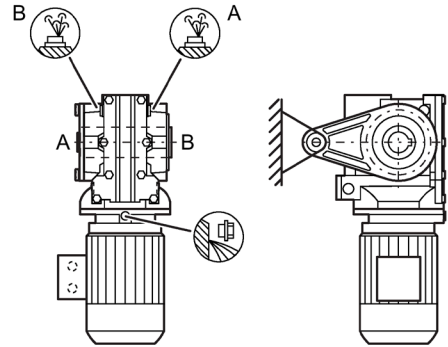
Einbautagen für Kegelradgetriebe KAD Aufsteckausführung Baugrößen 39 - 189
